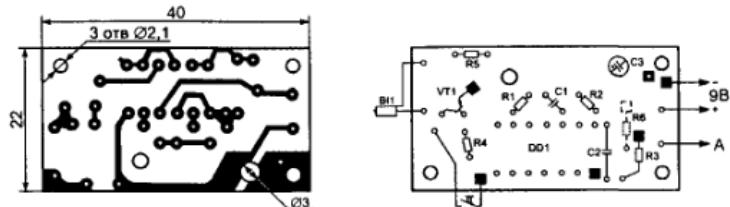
Печатная плата лазерного излучателя с лицевой и обратной стороны с расположением деталей
